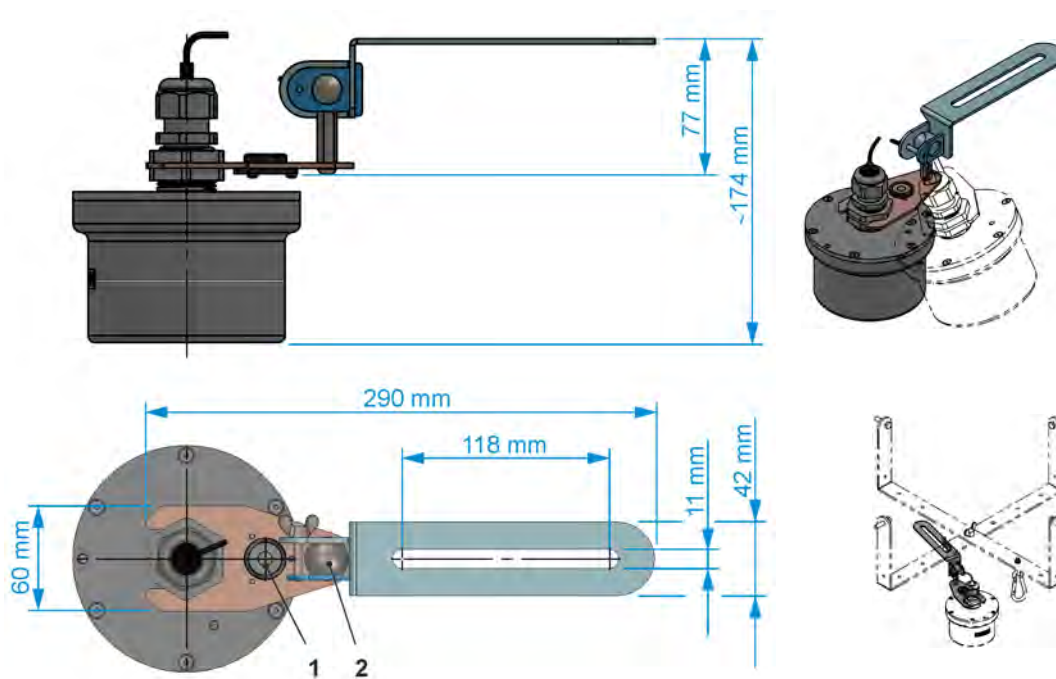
Variante 2 : Sur paroi verticale / plafond avec équerre de fixation
